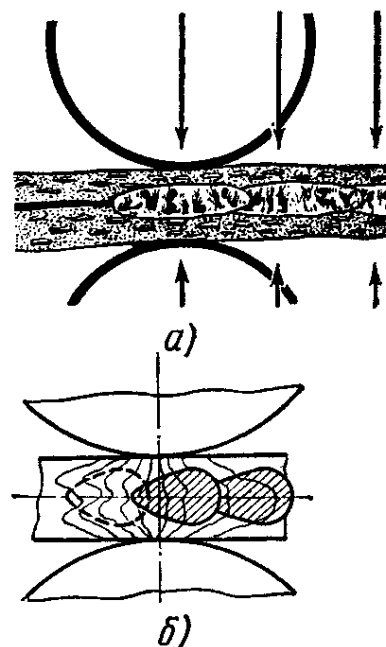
Схемы формирования шва при сварке стали (а) и алюминия (б)
